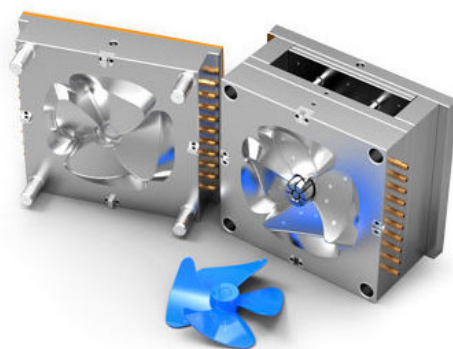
Objeto fabricado por injeção plástica em molde de alumínio. Fonte: [https://esmesm.manufacturer\\_globalsources.com/si/6008834678057/pdtl/Injection-mold/1128297303/Plastic-injection-molding.htm](https://esmesm.manufacturer_globalsources.com/si/6008834678057/pdtl/Injection-mold/1128297303/Plastic-injection-molding.htm);
